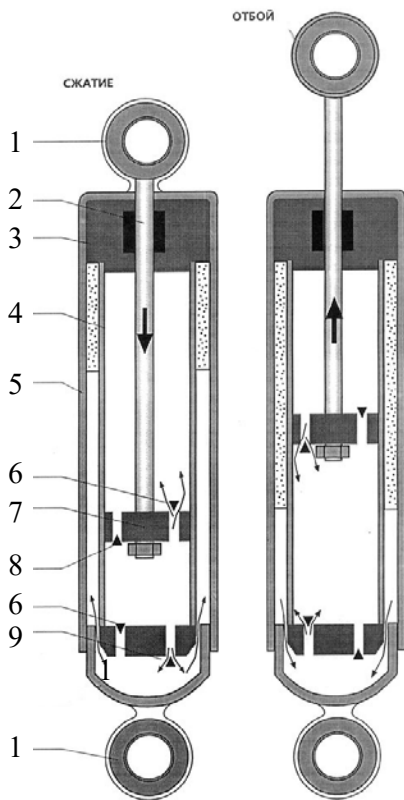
Схема устройства амортизатора с гидравлическими демпферами: 1 – шарнир; 2, 3 – соответственно шток и направляющие; 4 – цилиндр; 5 – резервуар; 6 – перепускной клапан; 7 – поршень; 8 – клапан отбоя; 9 – клапан сжатия
